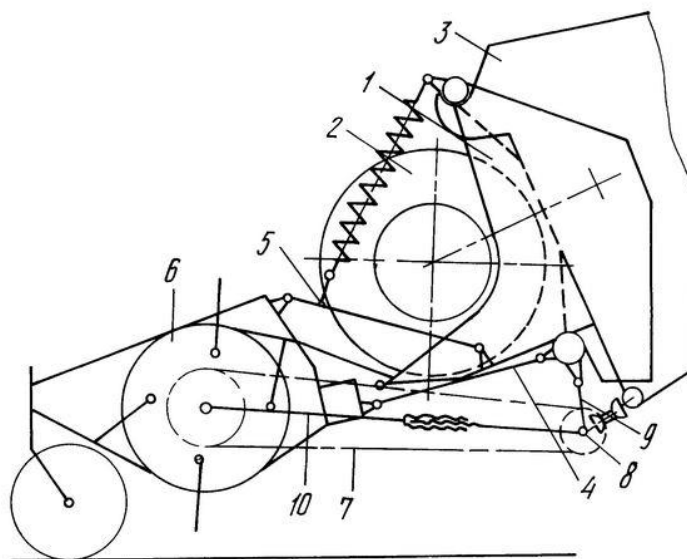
Схема подборщика валков № 2 060 627 С1
